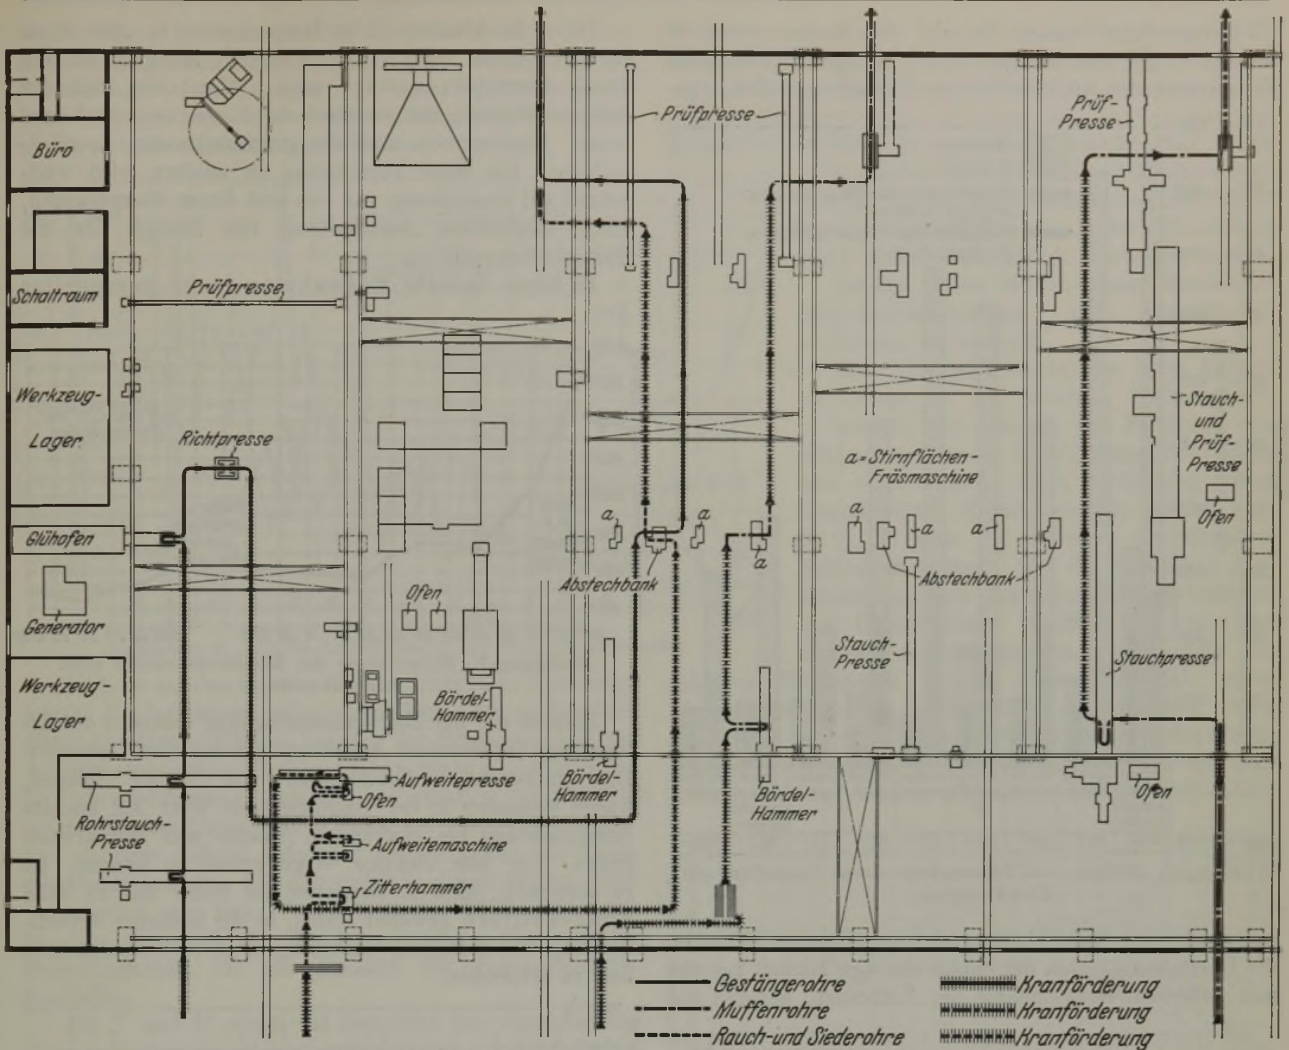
Lageplan mit Förderwegen einzelner Rohrorten nach dem Umbau.
